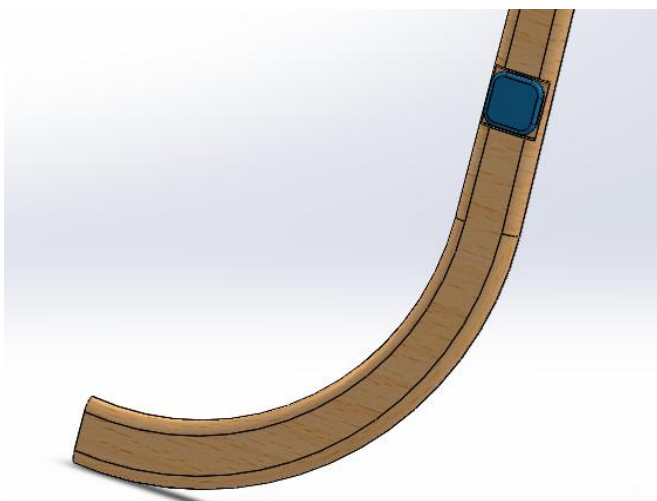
M Fotografia d'una vista detallada de l'acceleròmetre (Font: Elaboració pròpia)
